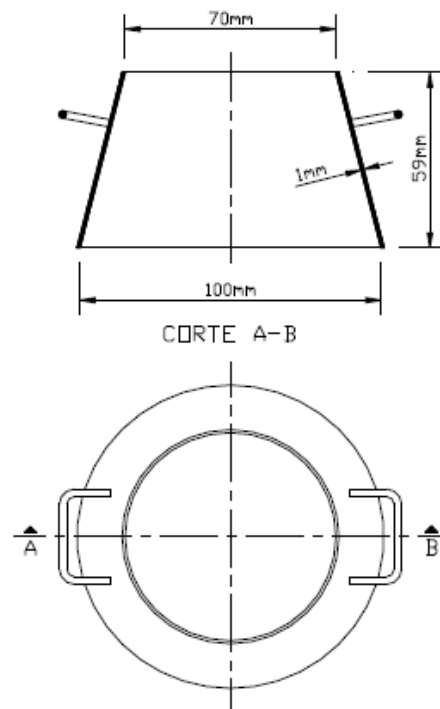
Cone para o ensaio de espalhamento em argamassa [5]
